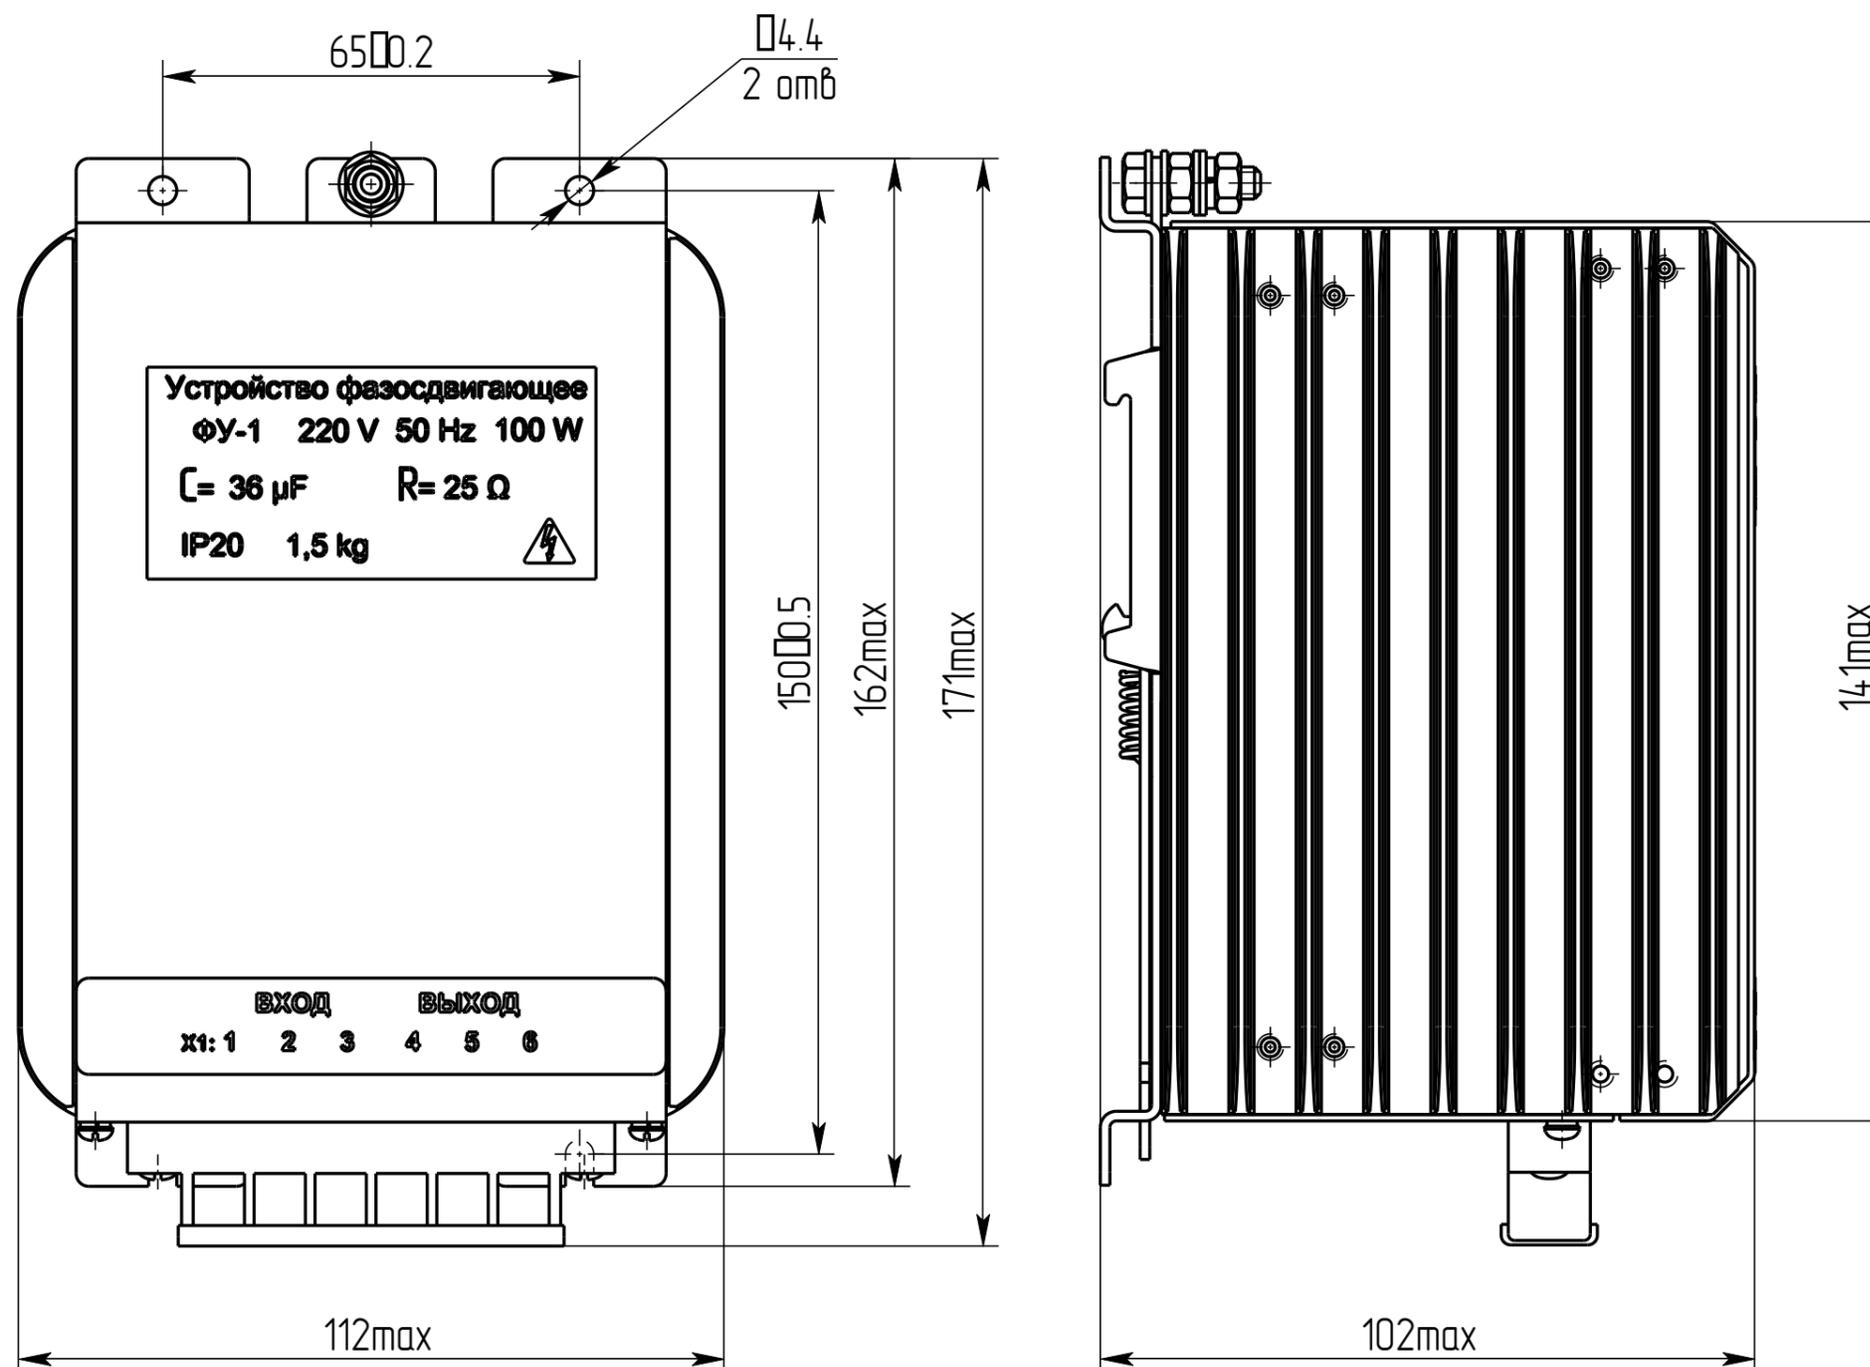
Габаритные и присоединительные размеры ФУ1, ФУ-2
